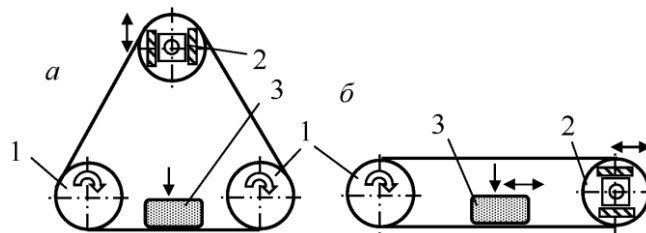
Механізми головного руху стрічкових шліфувальних верстатів: *а* - трьохбарабанний; *б* - двобарабанний
